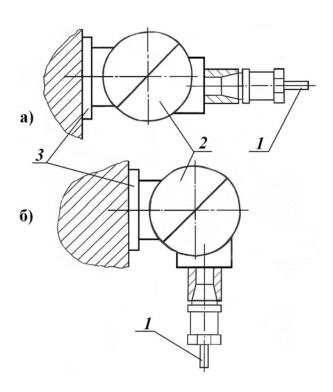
Угловая шпиндельная головка горизонтального ОЦ: I — инструмент; 2 — поворотный механизм; 3 — телескопическое устройство крепления
